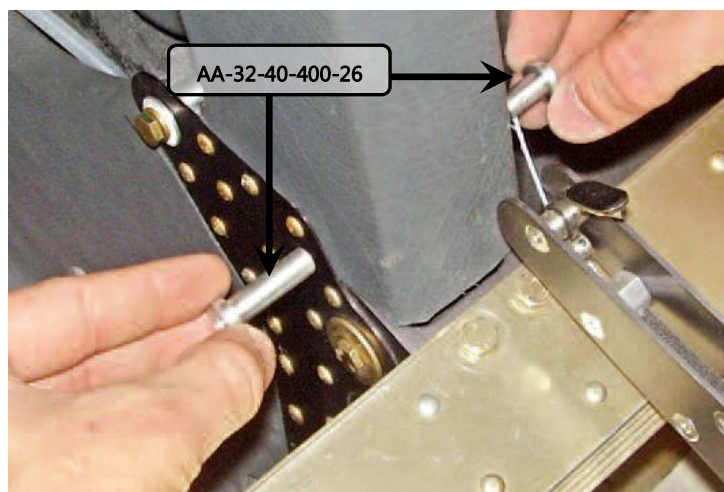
e 64 – Fixação inferior – espaçadores e vista lateral
